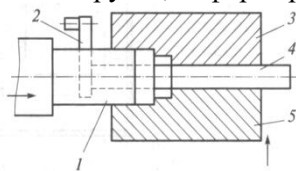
Схема штамповки ступенчатого вала с фланцем на горизонтально-ковочной машине: 1 — пуансон; 2 — упор; 3 — неподвижная матрица; 4 — пруток (заготовка); 5 — подвижная матрица
